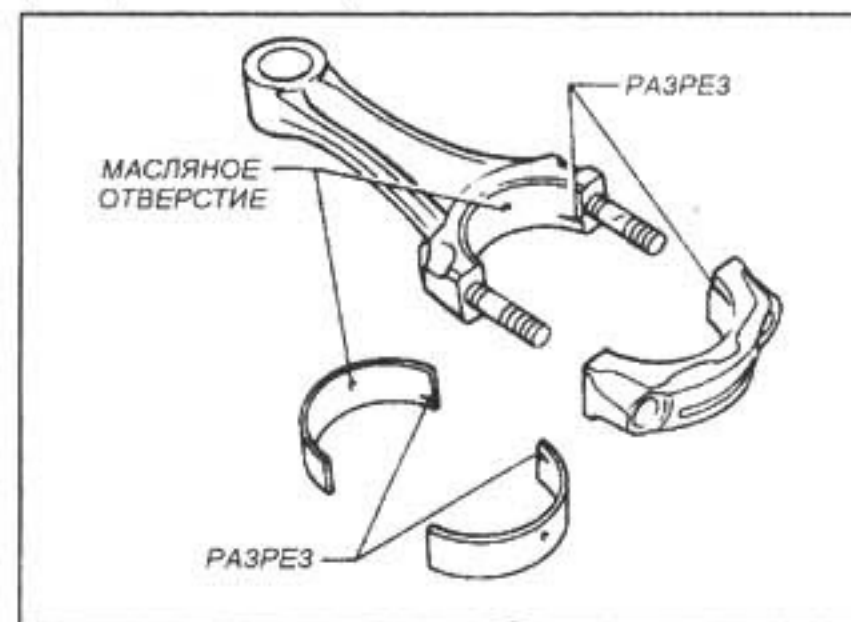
1 — выступы на вкладышах; 2 — пазы в головке и крышке; 3 — масляные отверстия.
